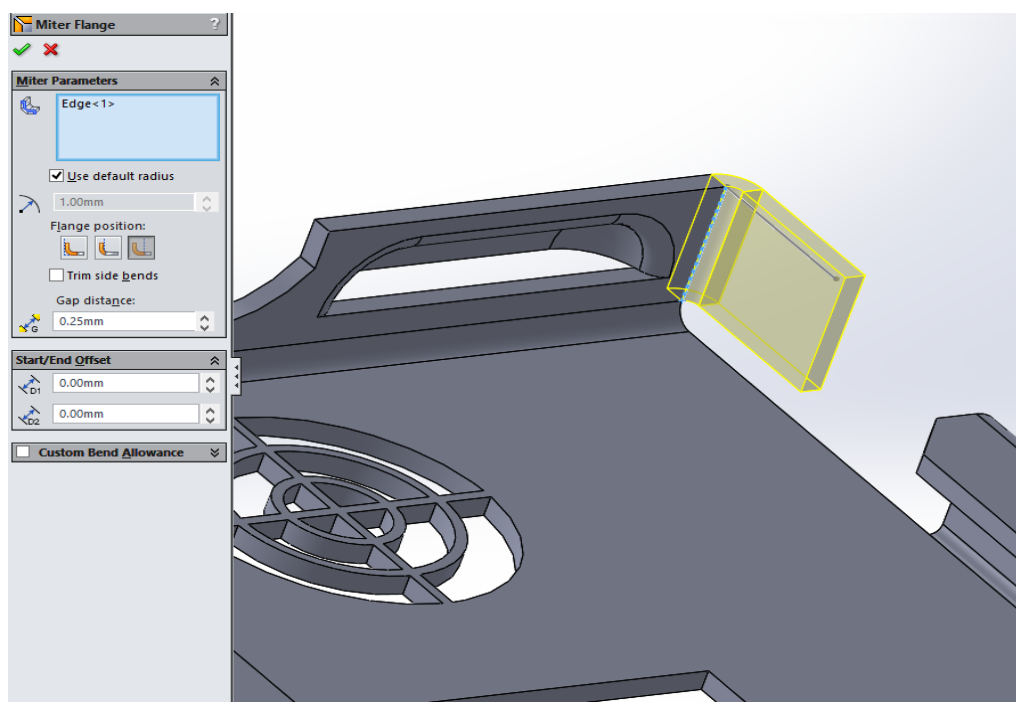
Flanșă realizată folosind comanda *Miter Flange featuring
